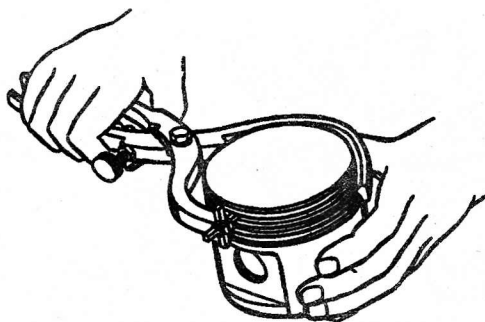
Очистка нагара в канавках поршней с помощью приспособления 5-У-27691
